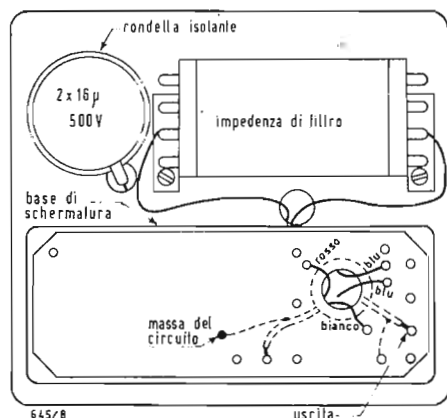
Componenti montati sulla parte superiore della piastrina di supporto e filatura dei cavetti schermati di entrata e di uscita saldati dal lato del circuito stampato della piastrina 134.
